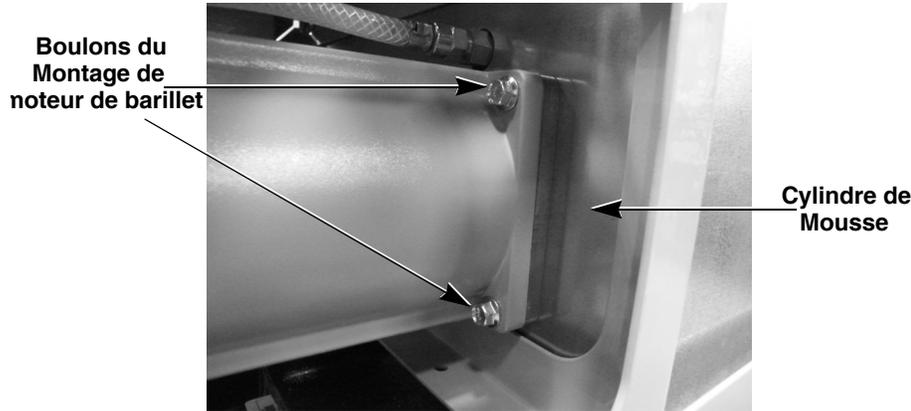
Vue latérale du moteur avec en relief deux des quatre boulons de montage
